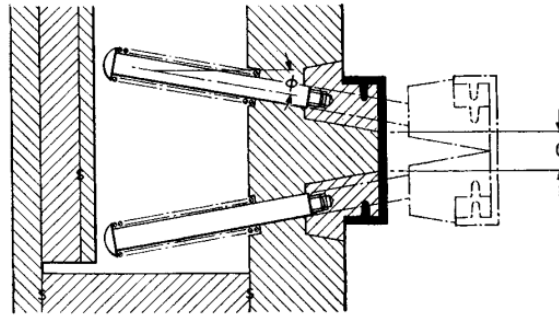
Molde con núcleo partido. Fuente: How to make injection molds [7].
